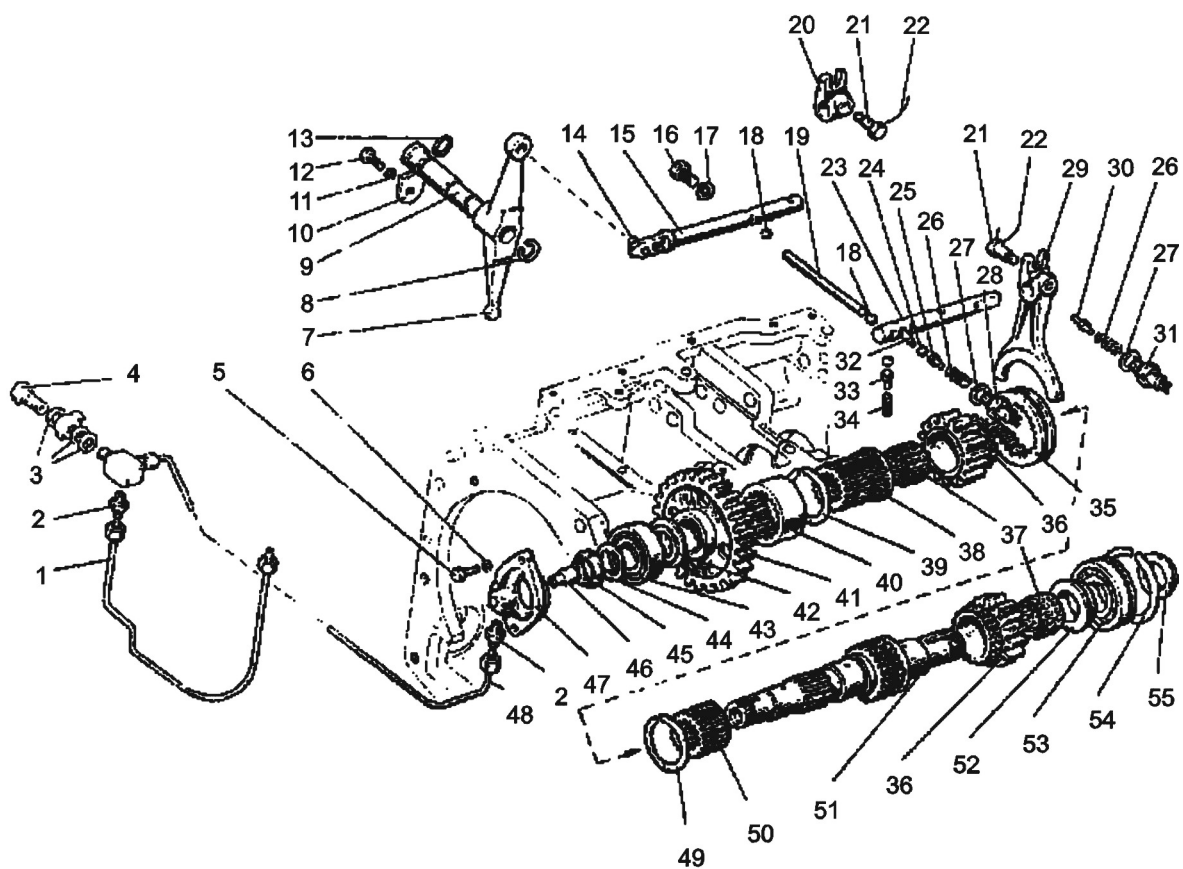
Коробка передач – Вал пониженных передач. Вал. Стакан
